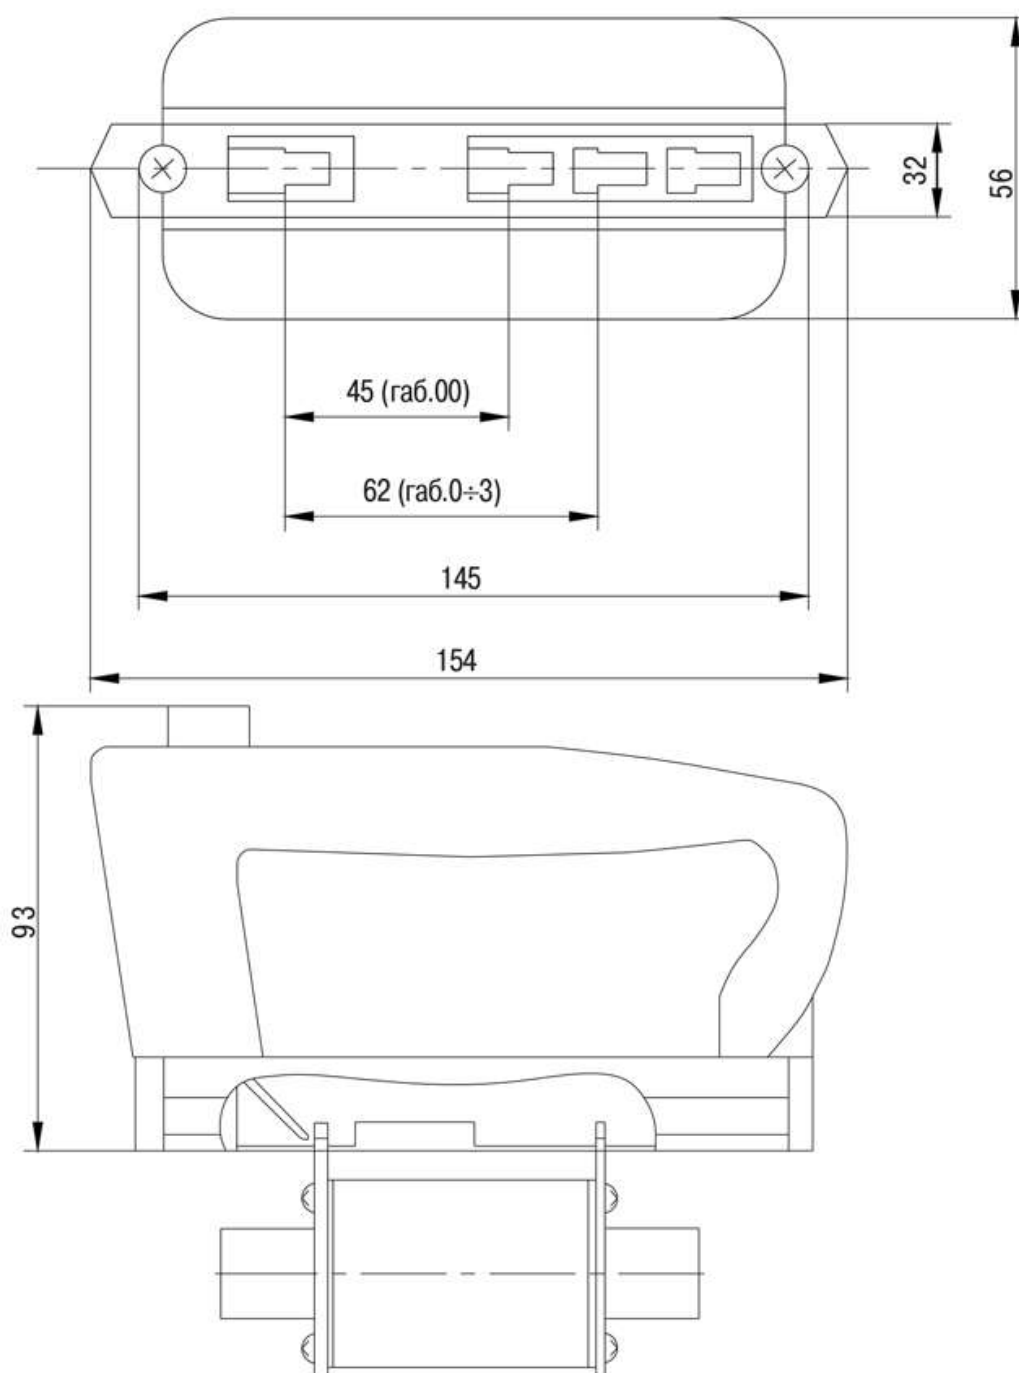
Габаритные размеры рукоятки для смены плавкой вставки
